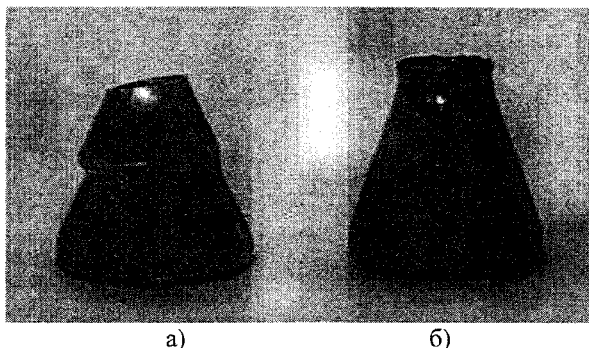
Форма деталей, полученных в штампах с разной обработкой поверхностей рабочего инструмента: а) с чистой поверхности Ra 3,2; б) с отшлифованными поверхностями до шероховатости Ra 0,2
